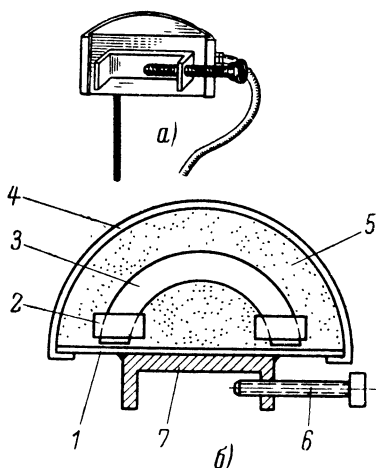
Электромагнитный звукосниматель для преобразования колебаний корпуса инструмента.
